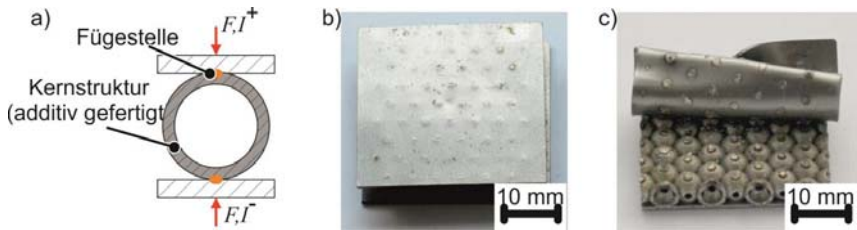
Widerstandsschweißen additiv gefertigter Kernschicht mit gewaltem Deckblech, a) Systematik, b) Geschweißte Baugruppe, c) Abschleißtest
